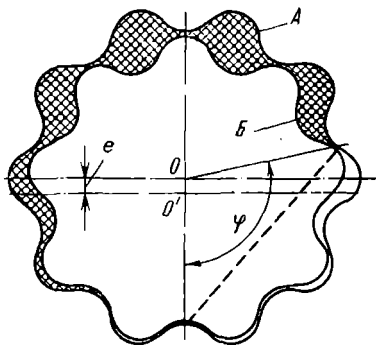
Контуры сечений рабочих поверхностей статора (А) и ротора (Б) винтового двигателя.
